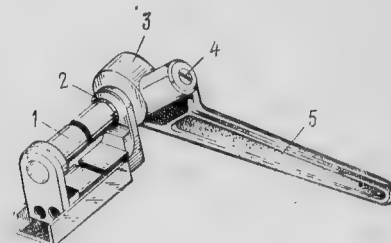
1 — прижим; 2 — насадка; 3 — шпindelь; 4 — винт стопорный; 5 — ручка
